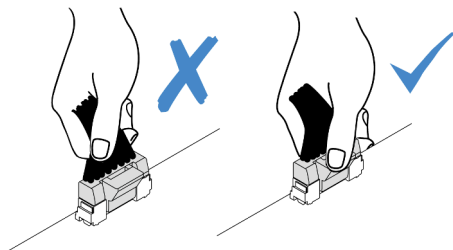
Desconectando o cabo do conjunto de placa-mãe
